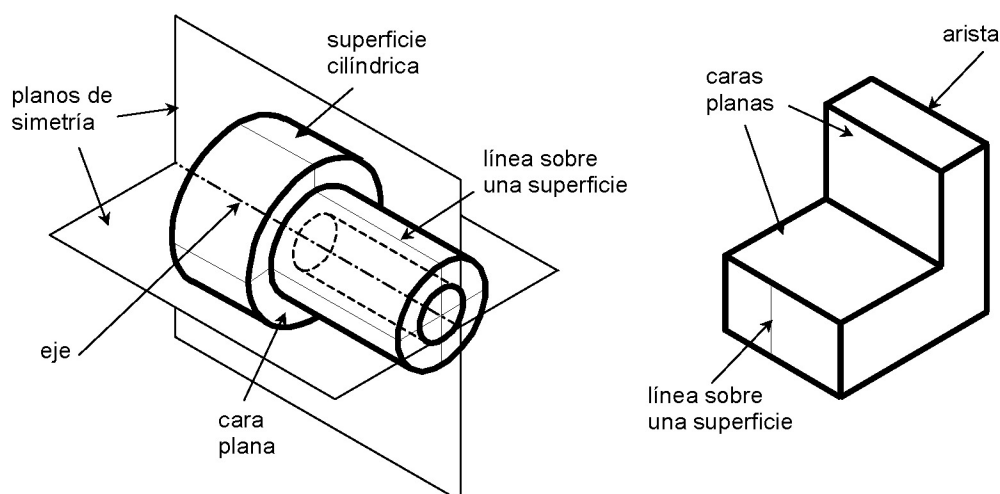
Elementos geométricos que pueden estar sujetos a tolerancia geométrica
